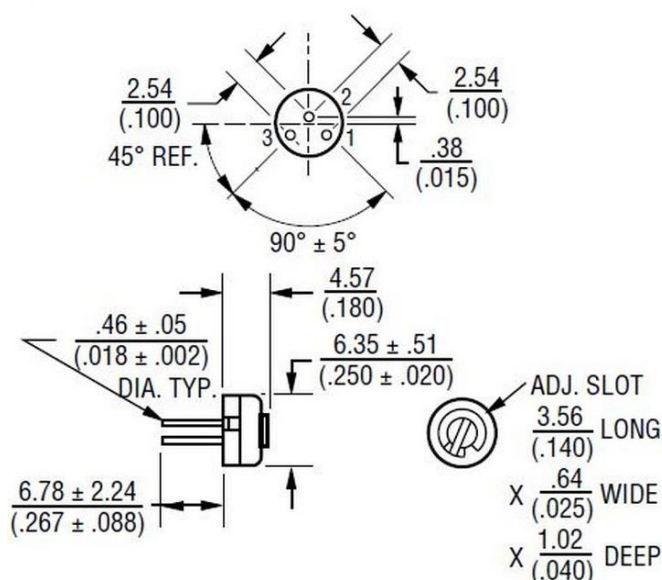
Габаритні розміри підстроювального резистора 3329H-1
